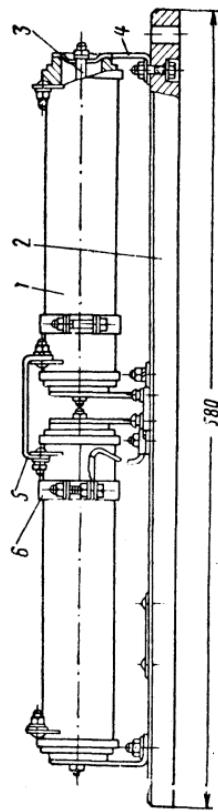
Сопротивление регулировочное типа ПП-113:
